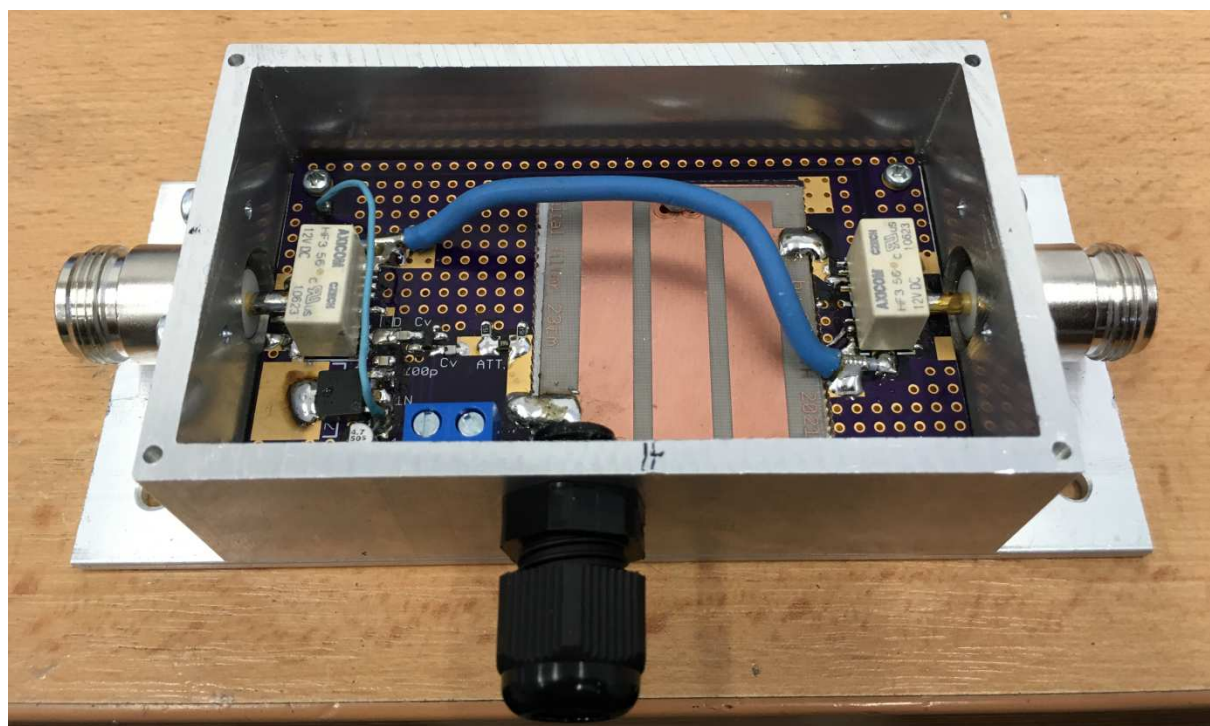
Provedení plošného spoje s osazením součástek s oknem pro montáž filtru
